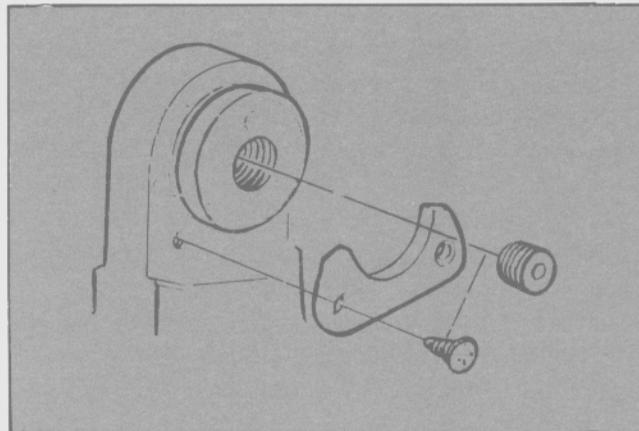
Montaje de la placa de empuje en la bancada trasera.
